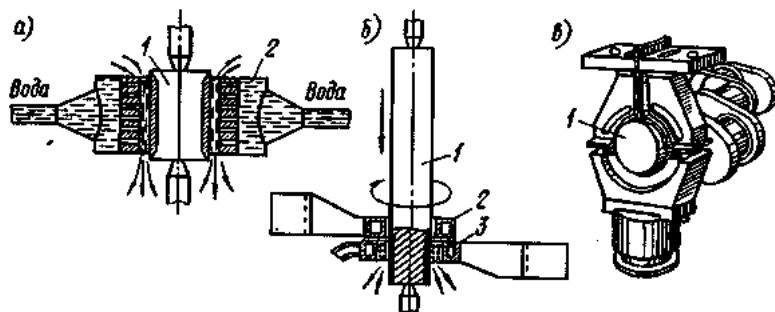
Поверхностная закалка деталей токами высокой частоты:
